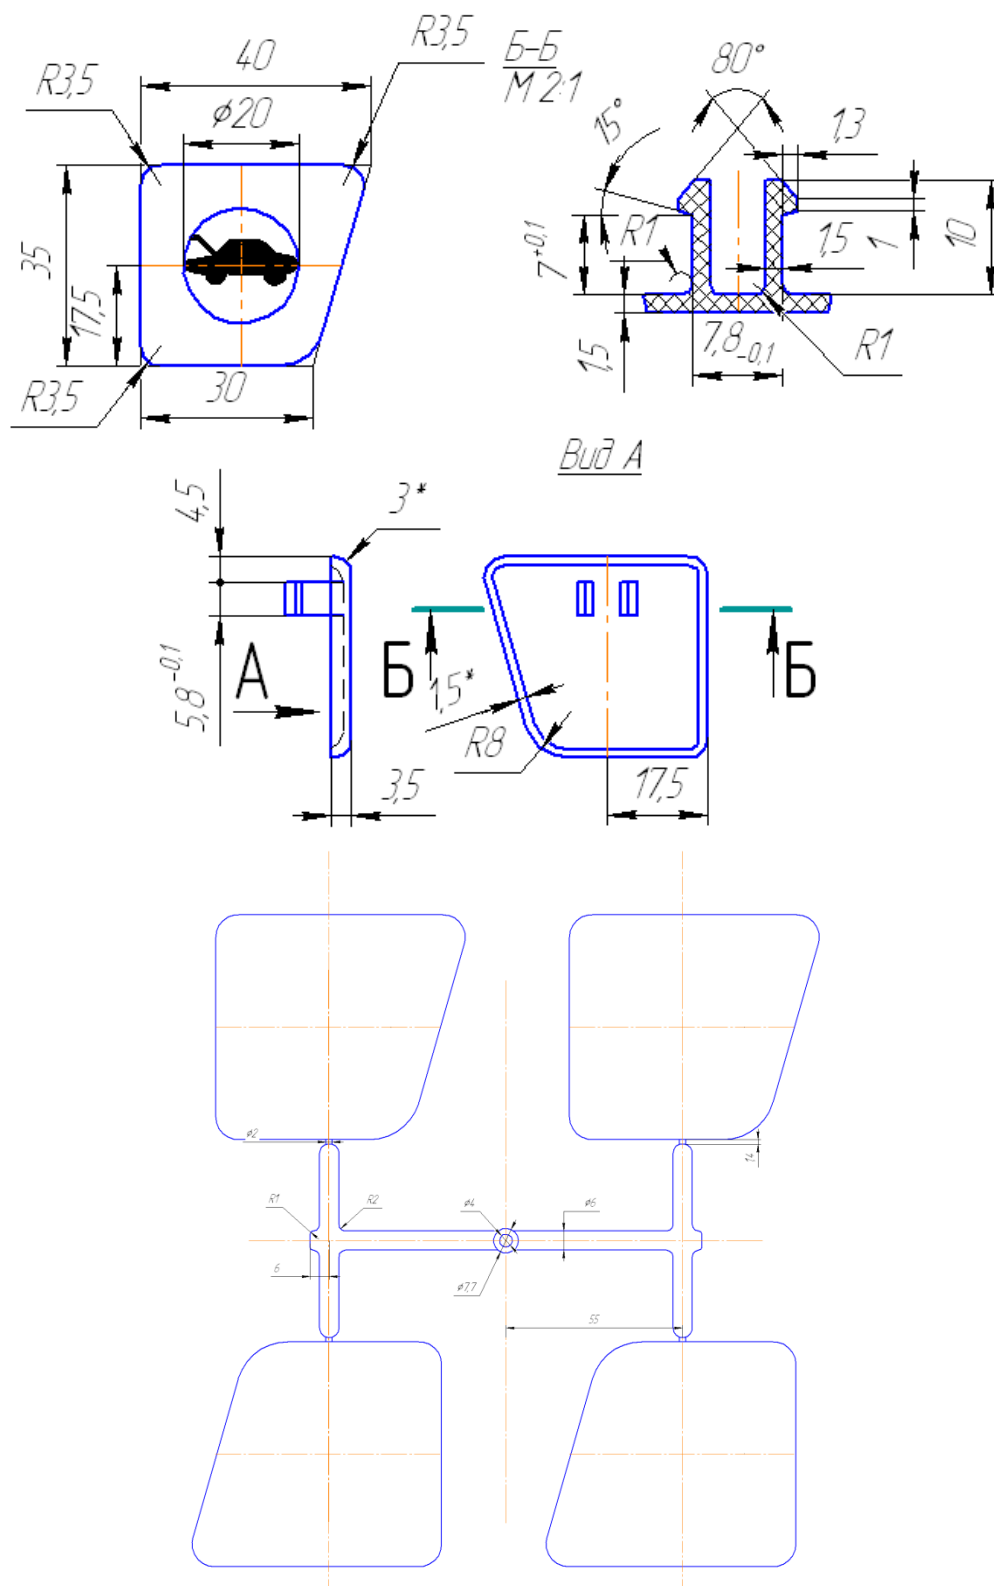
Облицовка рукоятки привода замка капота
